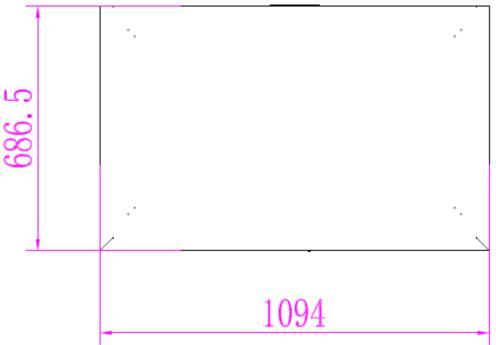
Габаритные размеры напольных шкафов 500-600A (вид снизу и сверху)
